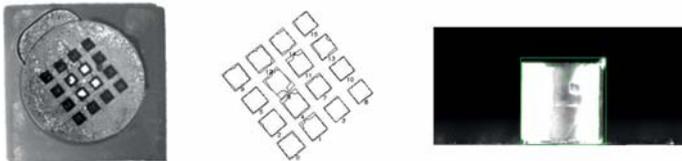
Inspeção de peça final sobre moldada, com defeito (rejeição por jito).
